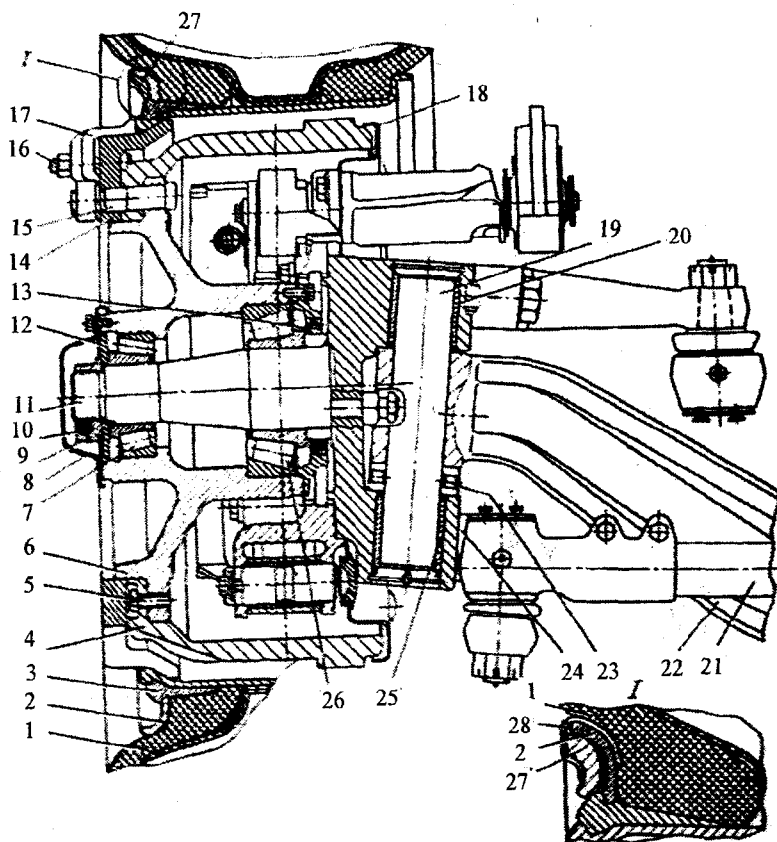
Передний неведущий мост грузового автомобиля с цилиндрическим шкворнем:
